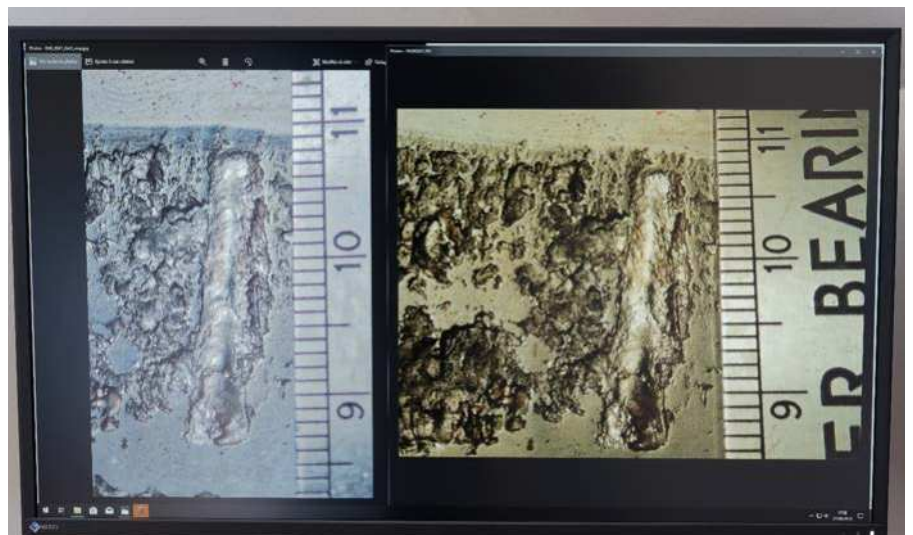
la fig. 35 a la derecha, la versión de la fig. 34 recortada a la izquierda
